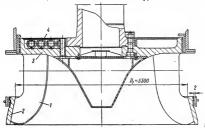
Сварно-литое рабочее колесо радиально-осевой турбины.
